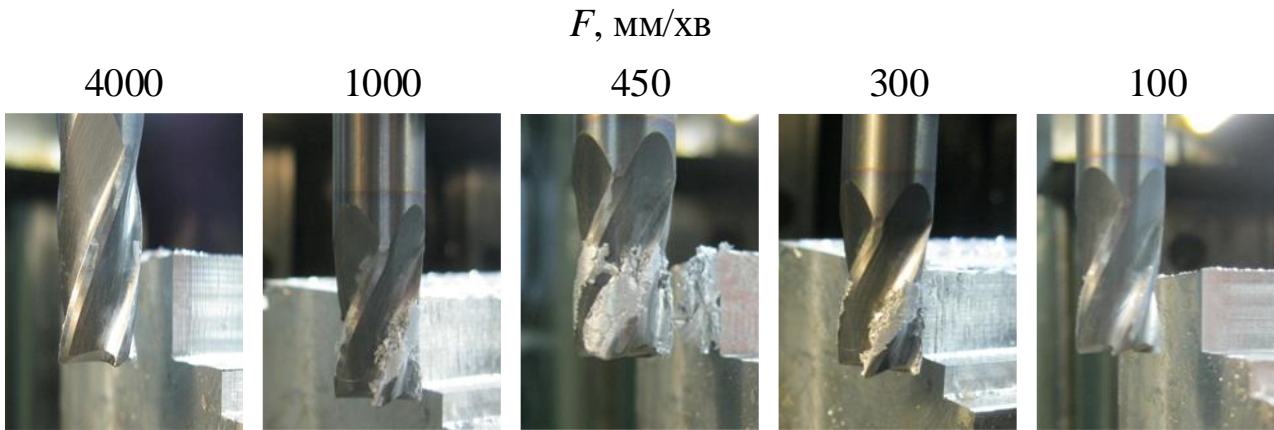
Стан інструменту після оброблення контрольного зразка
